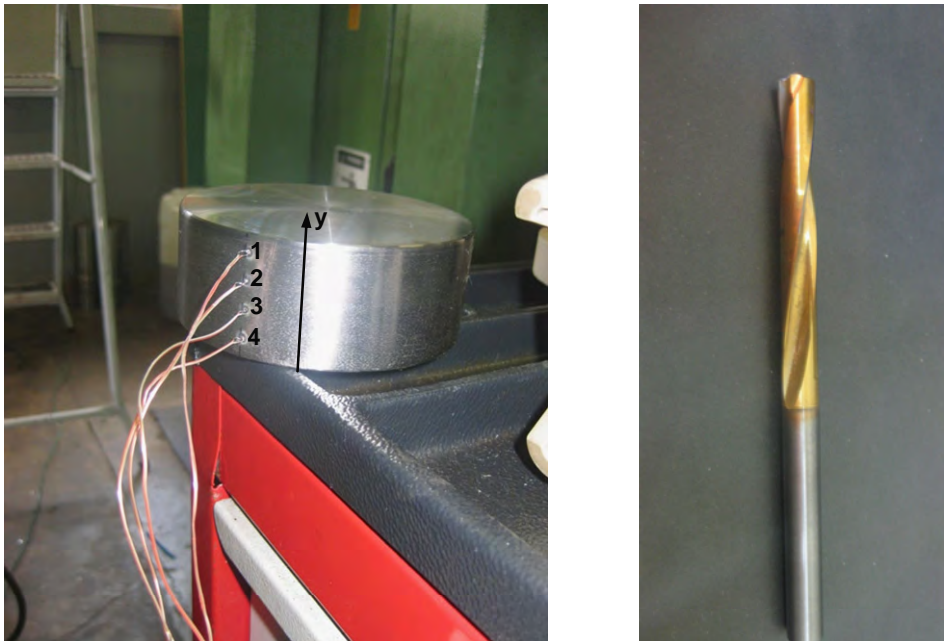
Detalhe da peça com os 4 termopares soldados e ferramenta: broca de metal duro revestida $\varnothing 10$ mm.
